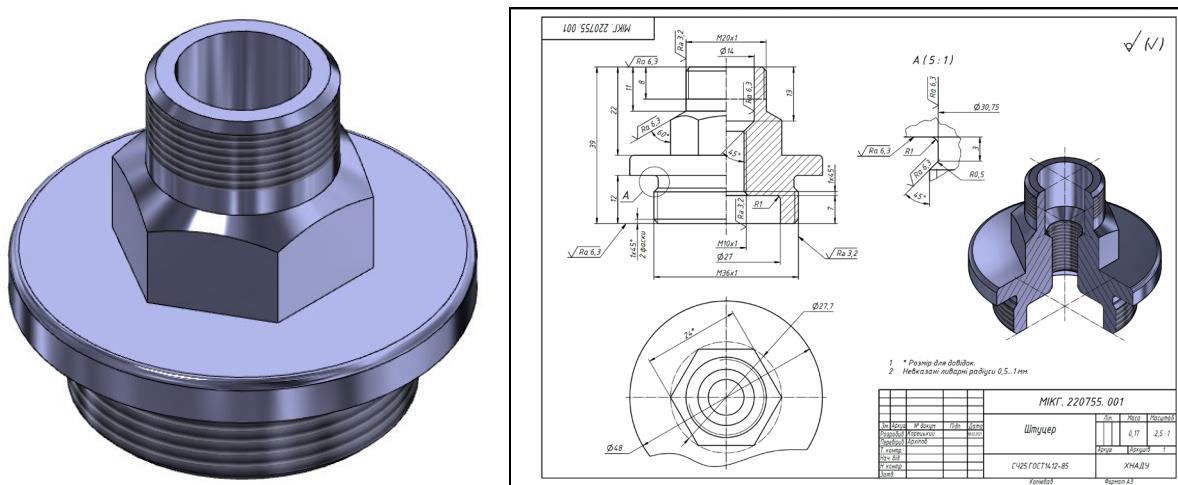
Модель та кресленик ливарної деталі з подальшою механічною обробкою.
